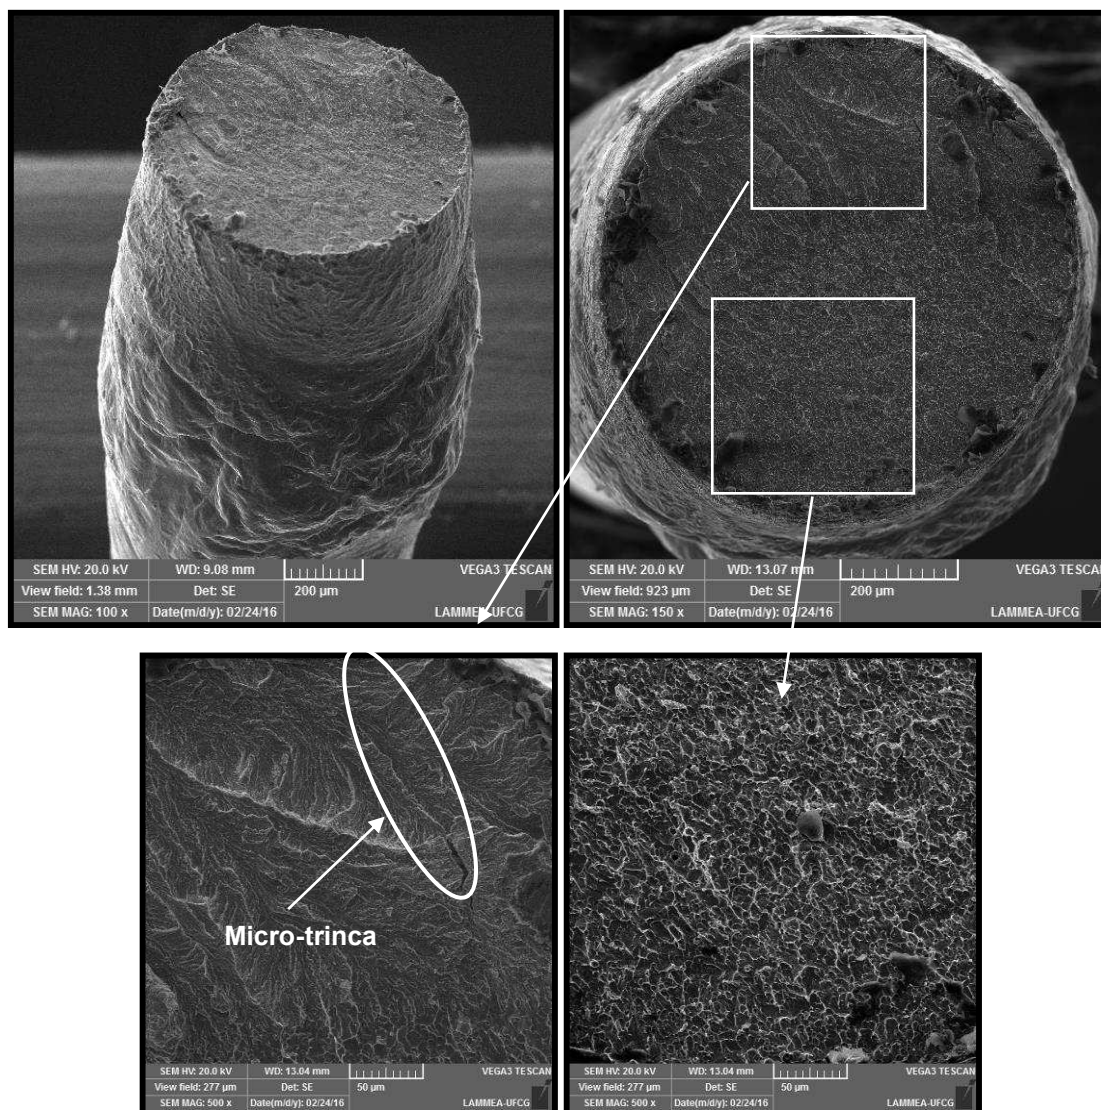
Superfície de fratura do fio superelástico soldado na configuração 9ms/60% testado a 40°C.
